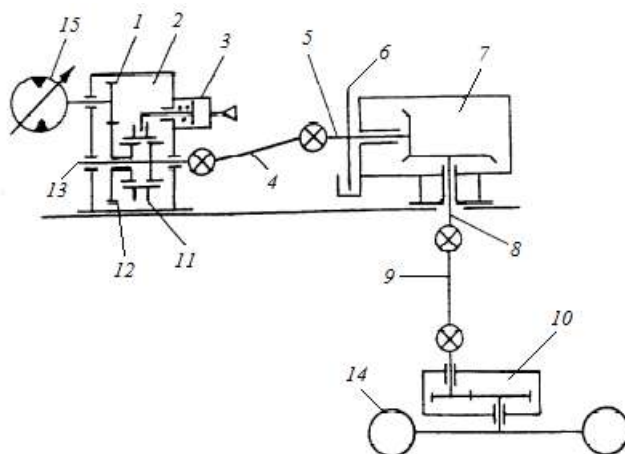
Компонівка елементів конструкції: 1 – ведуча циліндрична шестерня; 2 – початковий редуктор; 3 – пристрій вмикання муфти 11; 4 – карданна передача; 5 – вал ведучий; 6 – дискове гальмо; 7 – бортовий редуктор; 8 – ведений вал редуктора; 9 – карданна передача; 10 – колісний редуктор; 13 – вал ведучий; 14 – колесо; 15 – гідравлічний мотор
